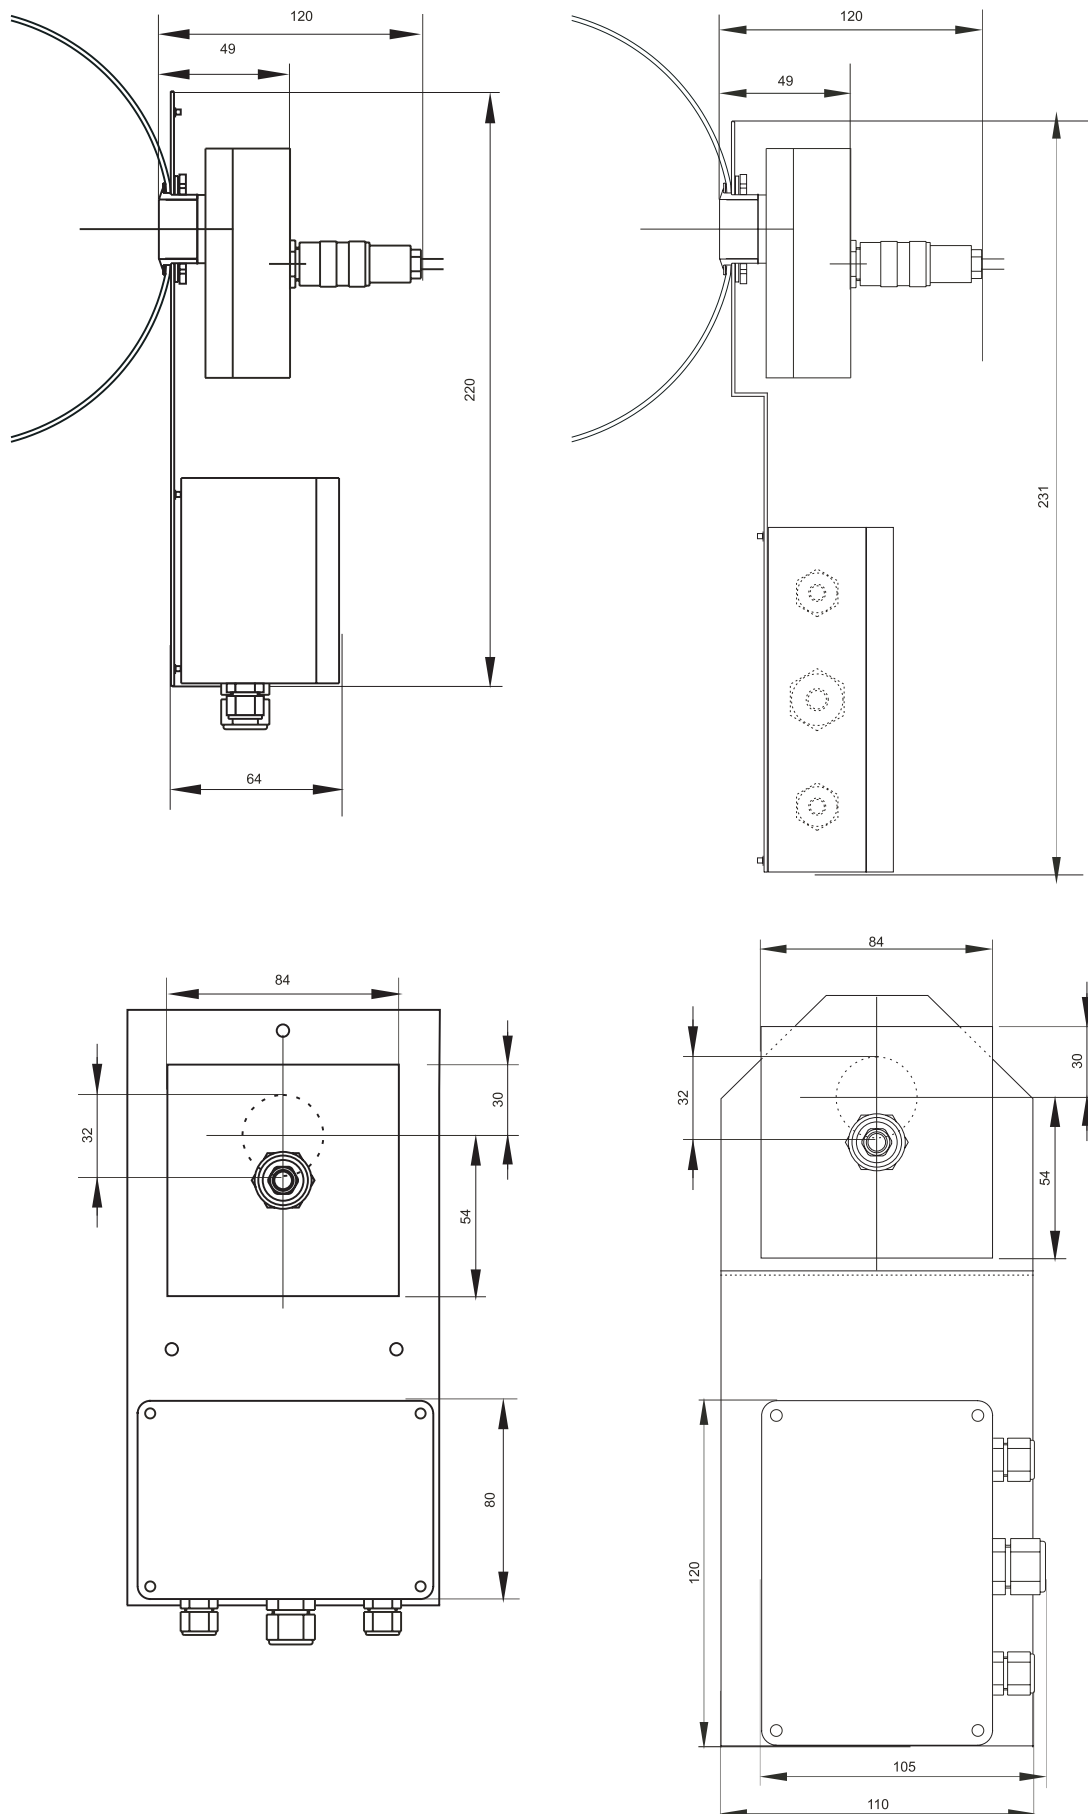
dimensions de montage d'un support vissable et d'une tôle de montage variante 1 et 2
